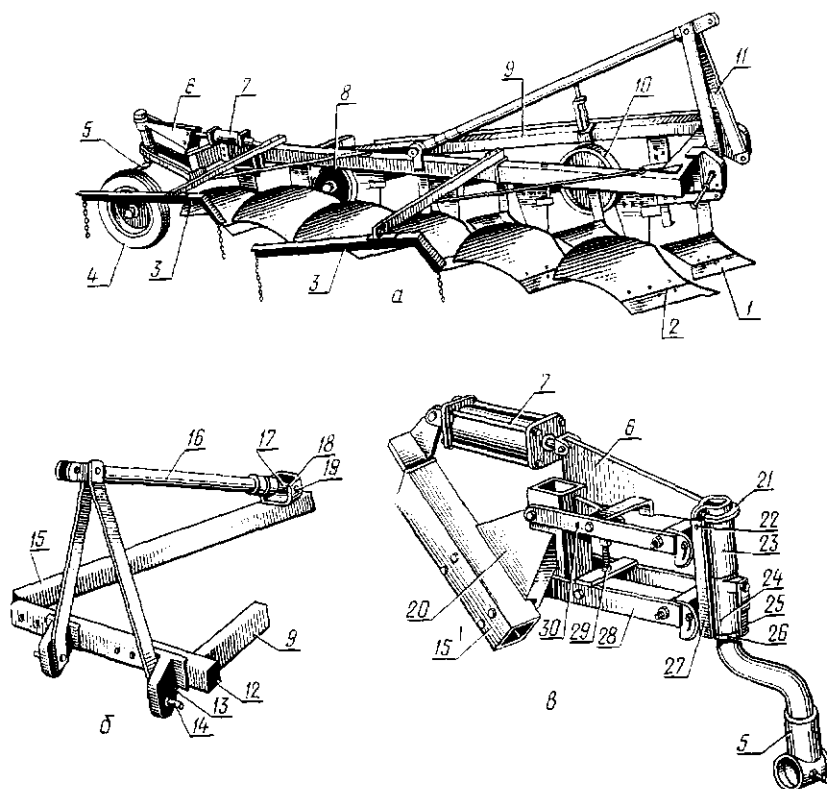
Шести корпусный плуг ПЛП-6-35:
